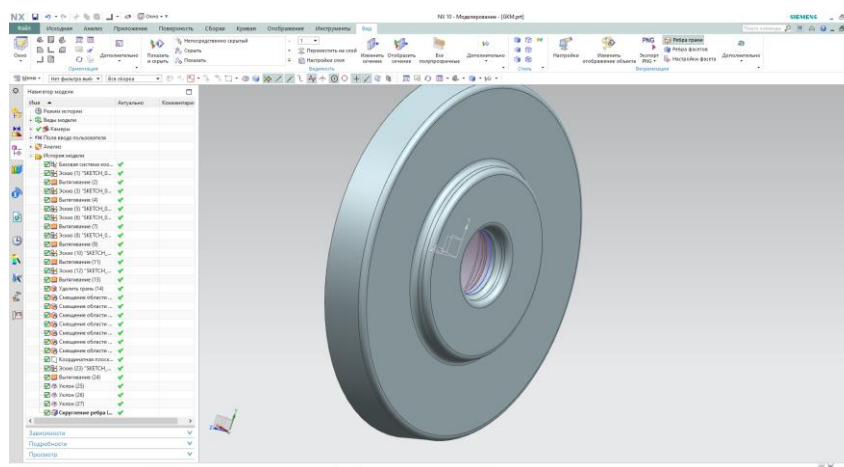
3D-модель заготовки по максимальним припускам
